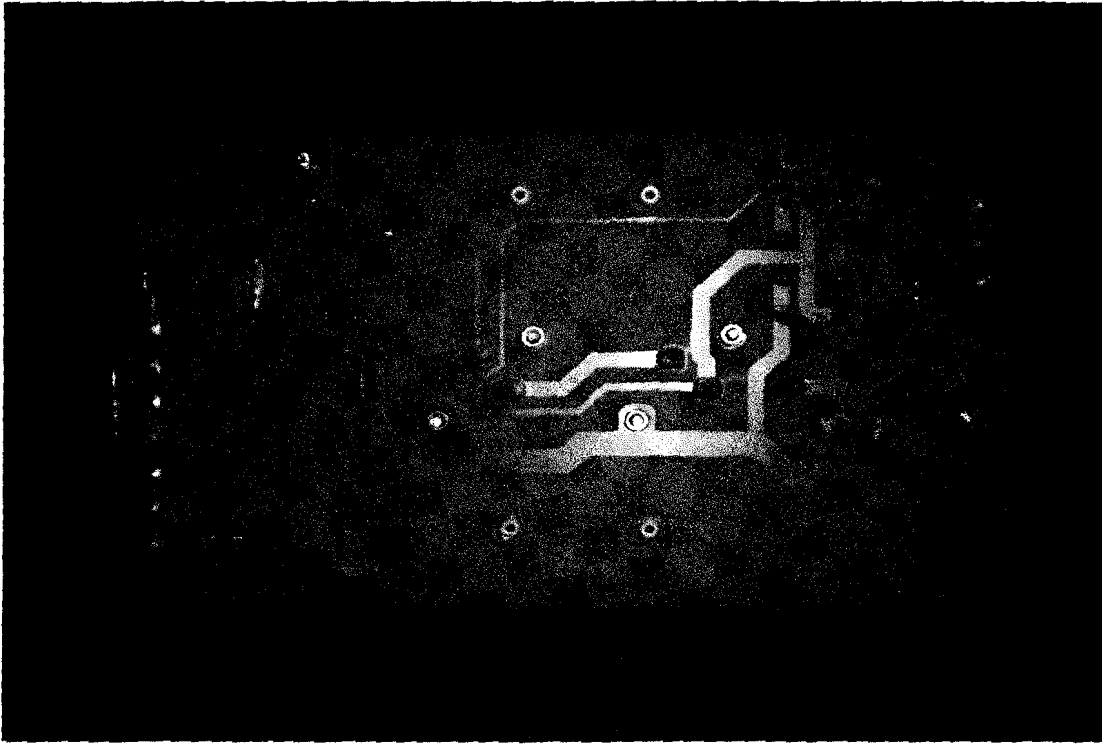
Vista del lado de la soldadura de la tarjeta 1.
